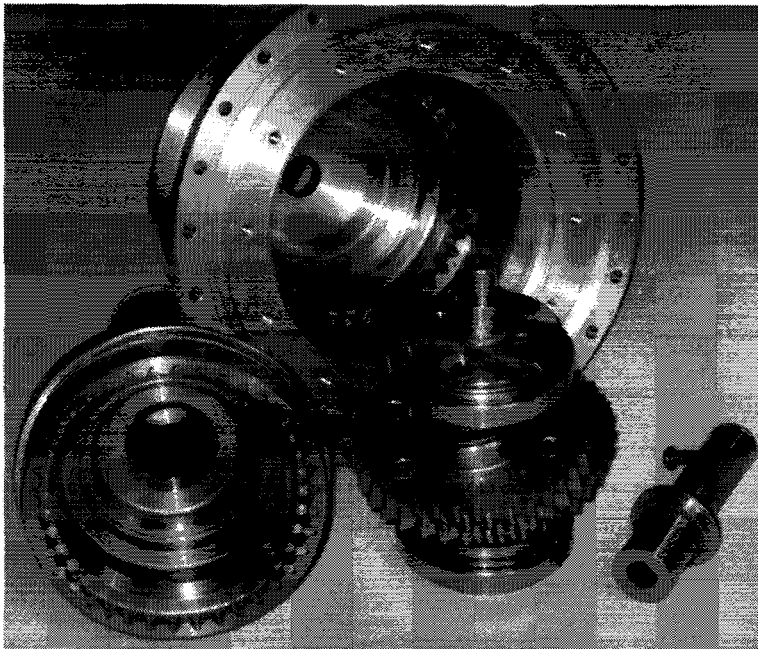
Элементы планетарного редуктора с цилиндроконическими зубчатыми зацеплениями
